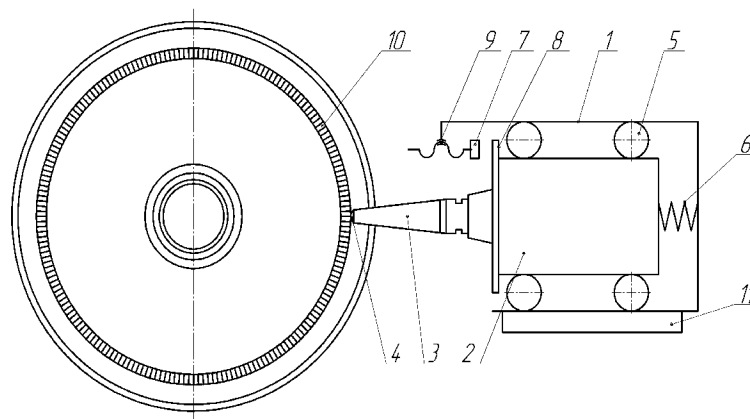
Установка для ударно-акустической обработки коллектора: 1 – корпусная деталь; 2 – преобразователь магнитострикционный; 3 – ультразвуковой инструмент; 4 – криволинейная рабочая поверхность инструмента; 5 – подвижная опора; 6 – пружина; 7 – ограничитель; 8 – поверхность опорная; 9 – винтовая пара; 10 – коллектор; 11 – суппорт станка
